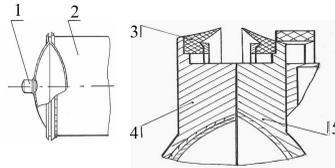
Пороховой аккумулятор давления: 1-воспламенитель; 2-обечайка; 3-пирошнур с манжетой; 4,5- полуцилиндрические поверхности
